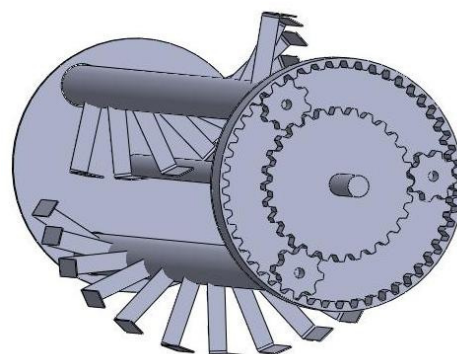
Планетарный рабочий орган фрезы со спиралевидными ножами
